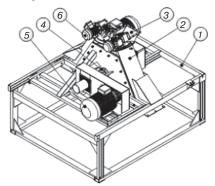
Дезинтегратор мокрого помола «ГОРИЗОНТ-3000 МК-ВА» $^{\circ}$: 1 – рама-основание; 2 – разъемный корпус; 3 – загрузочный патрубок; 4 – подшипниковый узел привода роторов-импеллеров; 5 – электродвигатель; 6 – устройство очистки камеры помола с индивидуальным приводом
